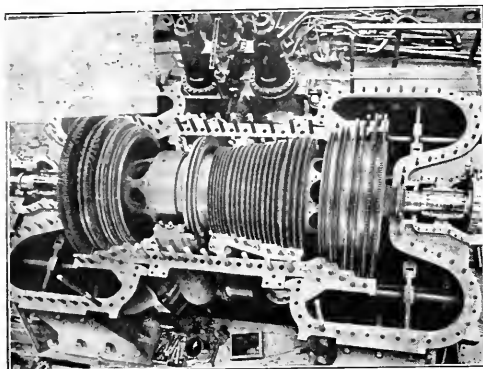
INTERIOR DE UNA TURBINA WESTINGHOUSE INSTALADA EN JAPÓN
